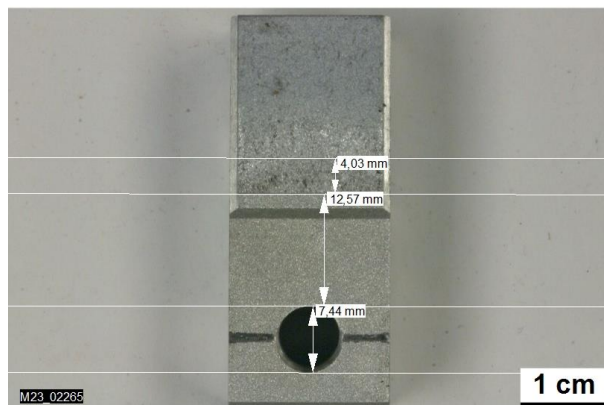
Probe 5.a Makroaufnahme Probenhälfte mit ausgemessener Länge von Lastangriffslinie bis zur erodierten Kerbe.
